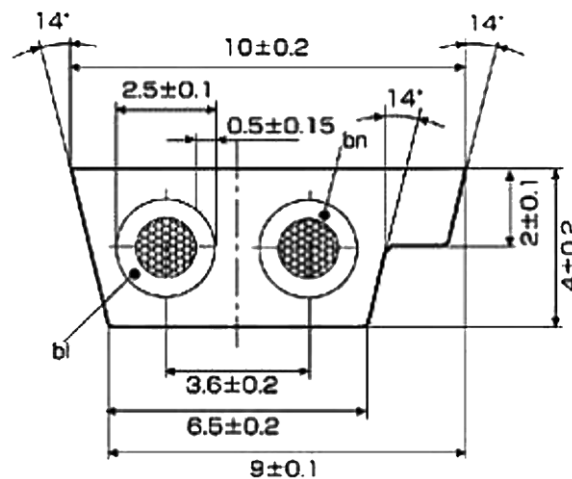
Vista do corte frontal do cabo AS-i (medidas em mm).
